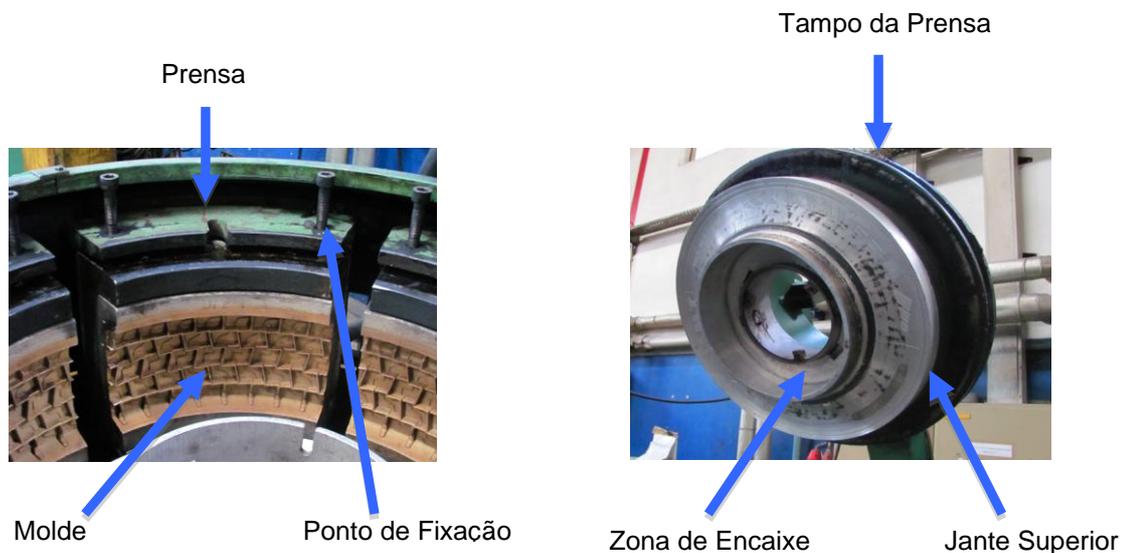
Componentes do conjunto Prensa/Molde.
